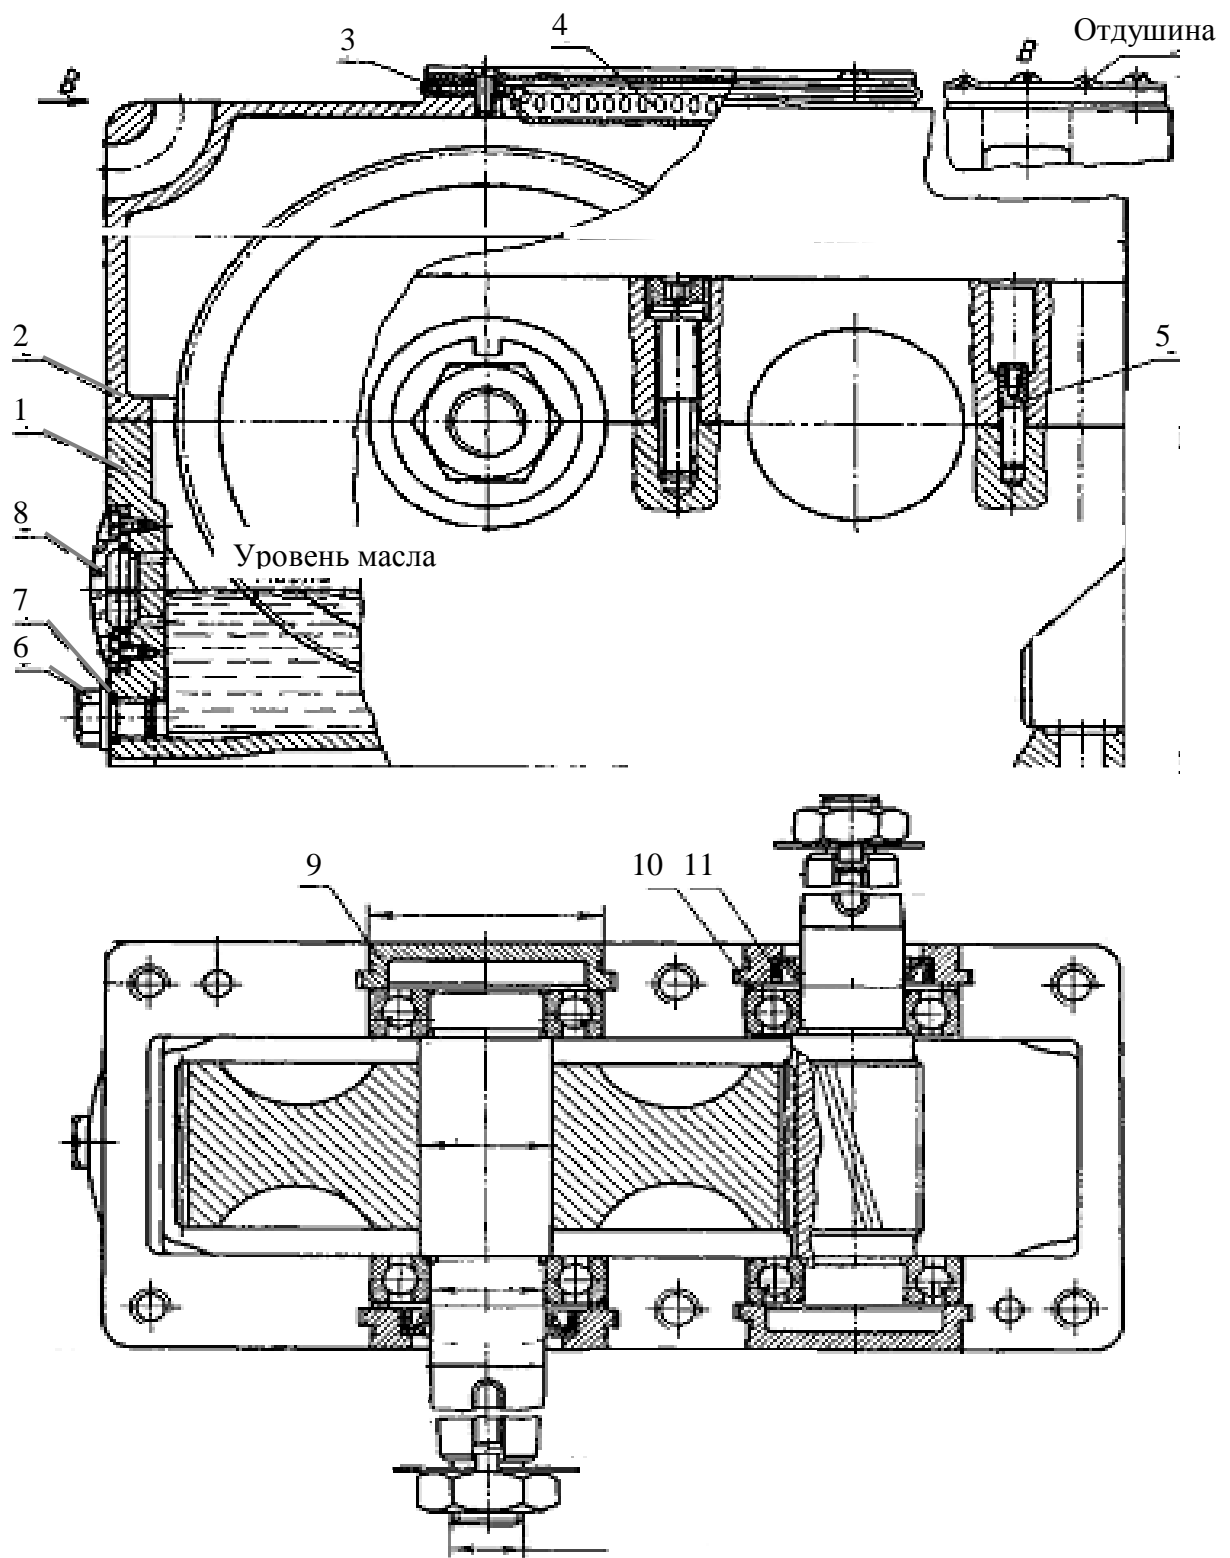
Редуктор цилиндрический одноступенчатый:
